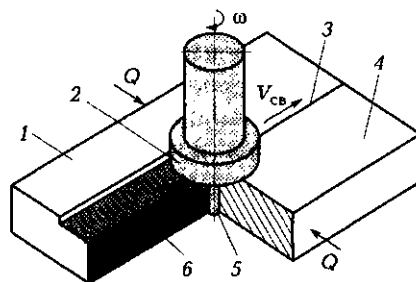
Схема процесса сварки трением с перемешиванием:
